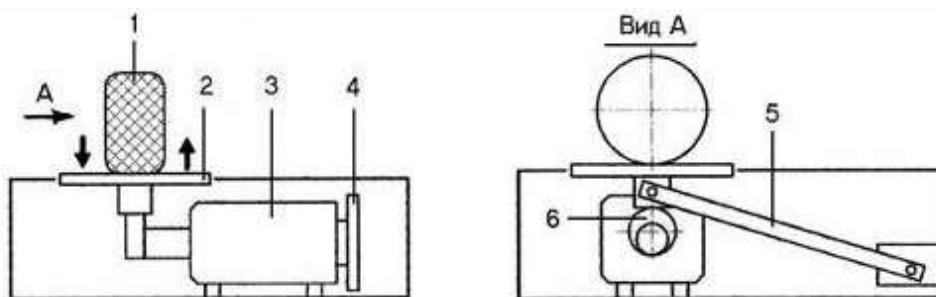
Схема стенда для перевірки амортизаторів:
